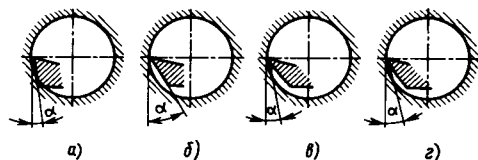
Выбор формы задней поверхности у инструмента для обработки отверстия
